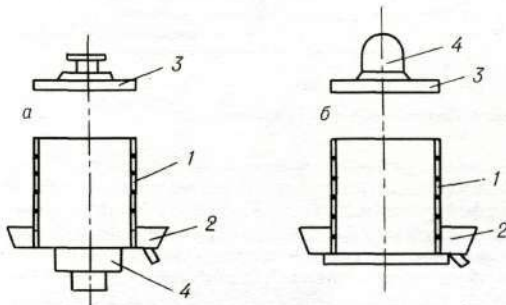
Вертикальный корзиночный пресс: а — нижнего давления; б — верхнего давления
